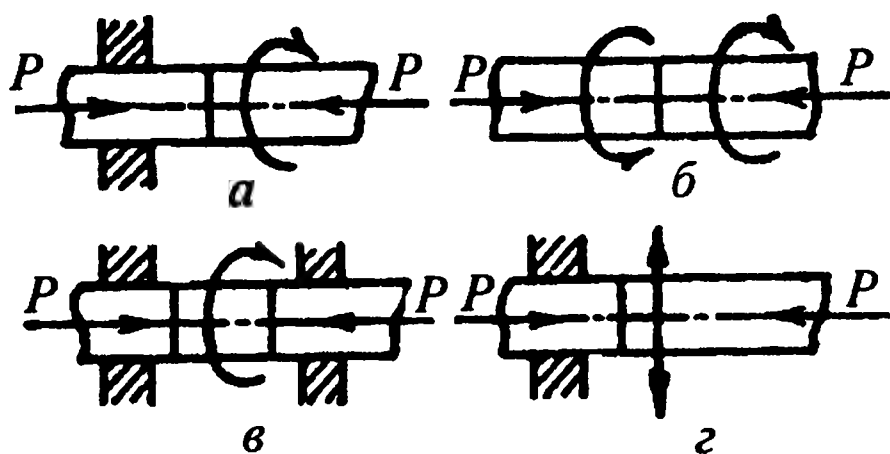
Принципиальная схема сварки трением:
